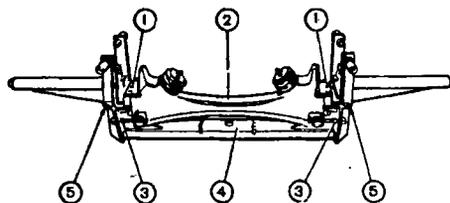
Проверка поперечины передней подвески: 1 - отверстия на поперечине под установочные штыри приспособления; 2 - поперечина; 3 - контрольные втулки приспособления; 4 - приспособление А.78124/R; 5 - контрольные отверстия установки болтов на поперечине
